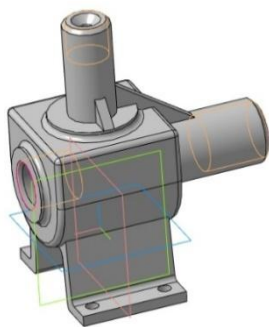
Корпус вентиля Рисунок 3 – Прокладка
